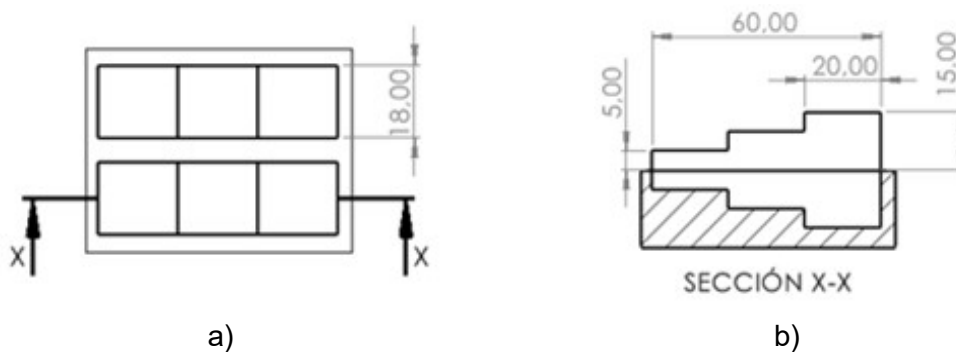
Geometría de las escaleras (a) Planta (b) Perfil.
